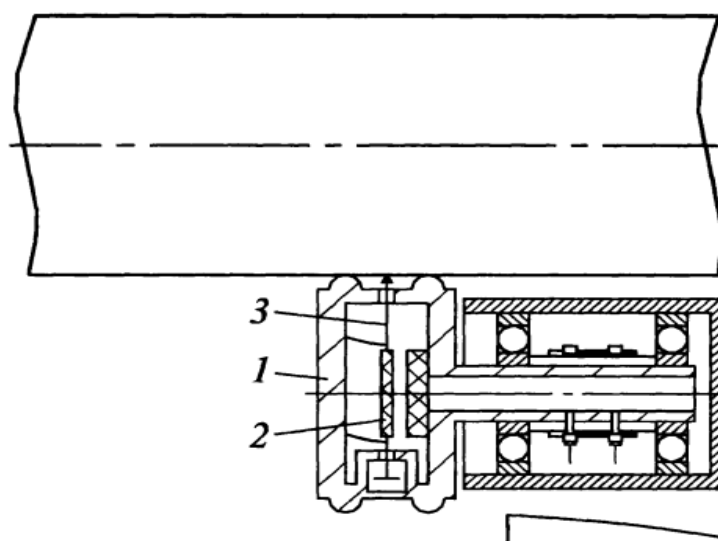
Устройство для измерения шероховатости в процессе обработки [35]
